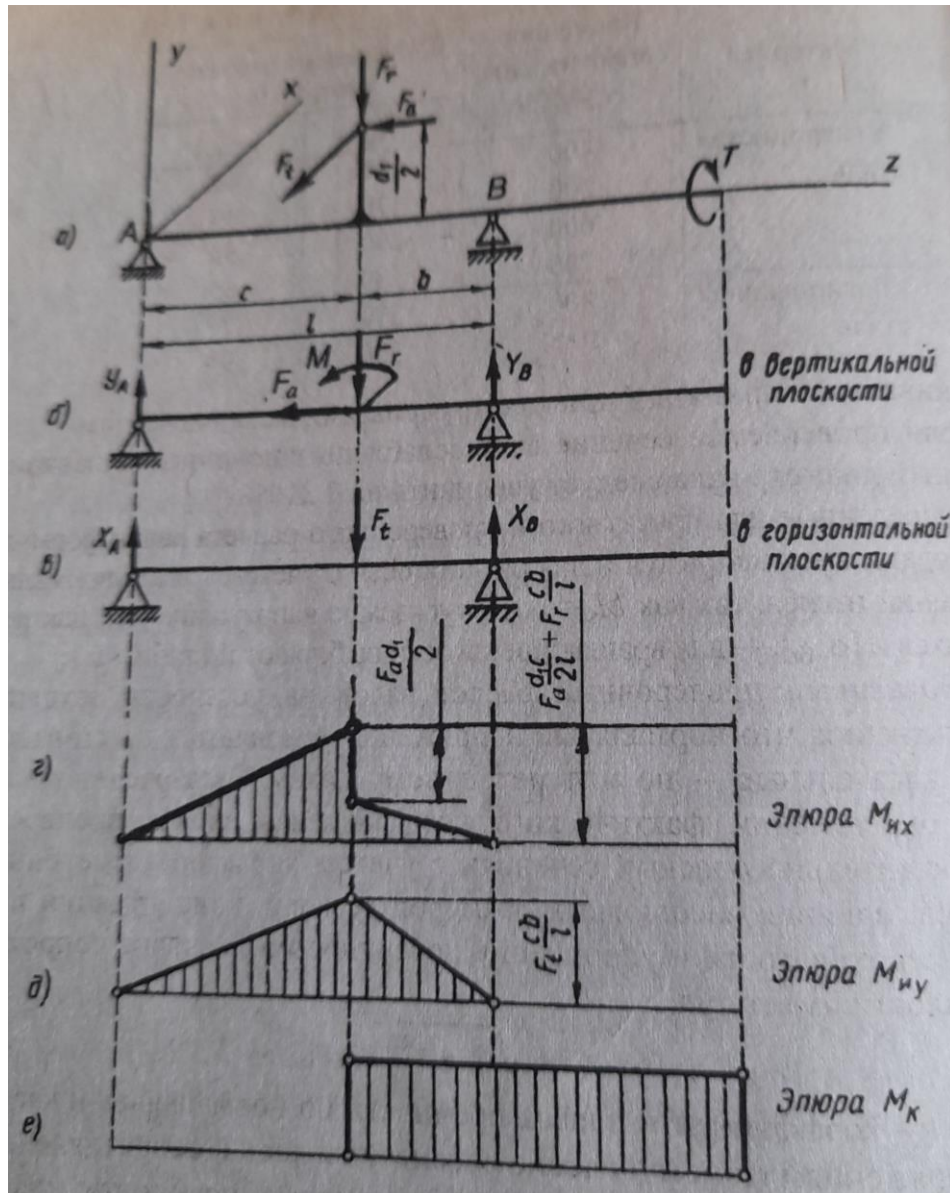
Расчетная схема вала цилиндрического редуктора
